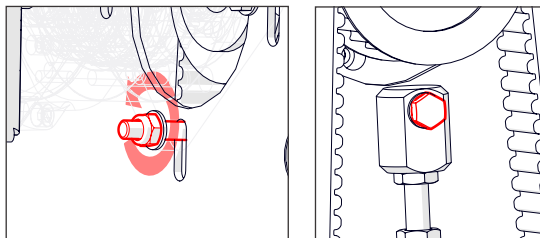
C - Mutter des Spannblocks/Motors leicht lösen.
